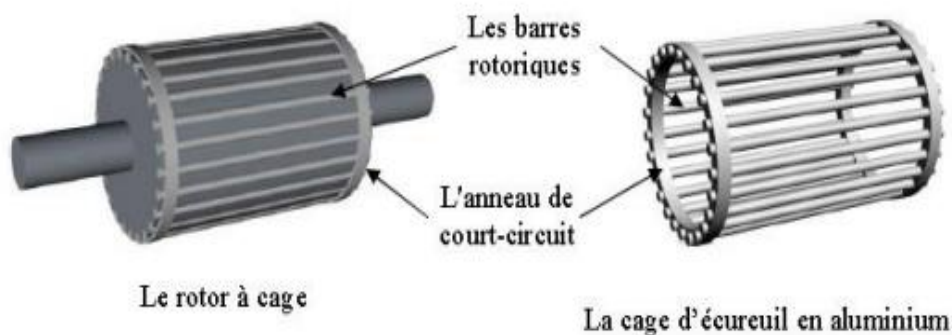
Rotor de la machine asynchrone triphasée à cage
